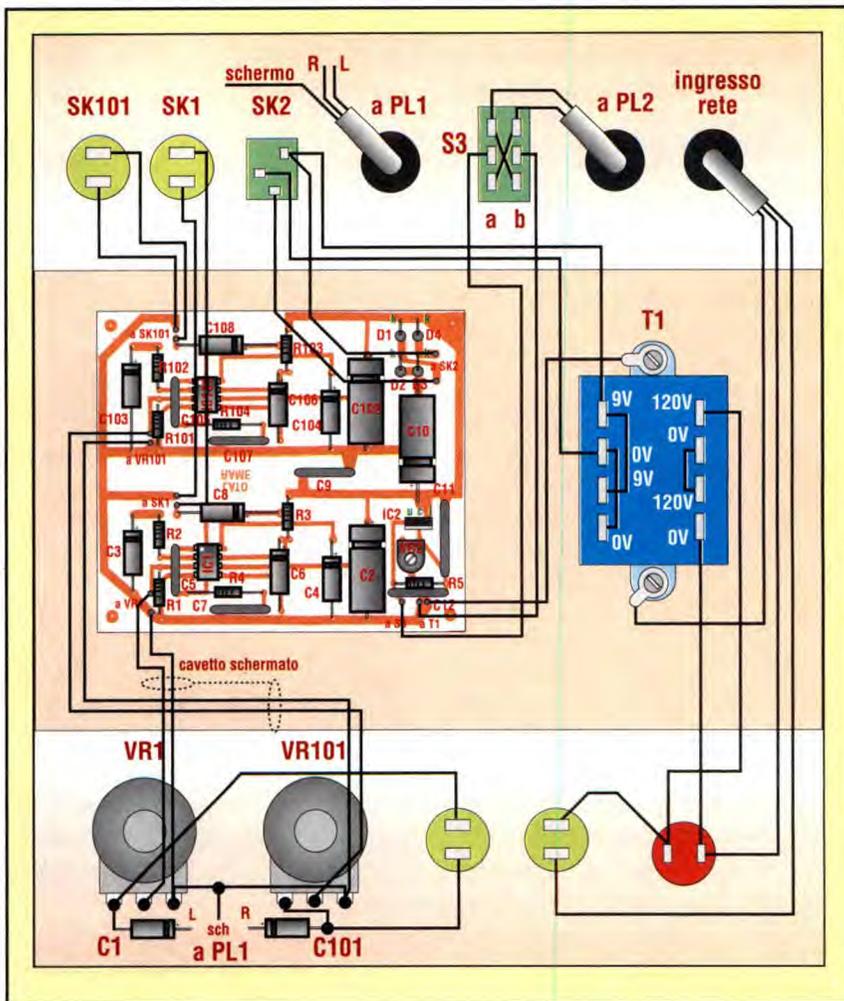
Cablaggi per il collegamento tra il circuito stampato e i componenti fissati ai pannelli.
